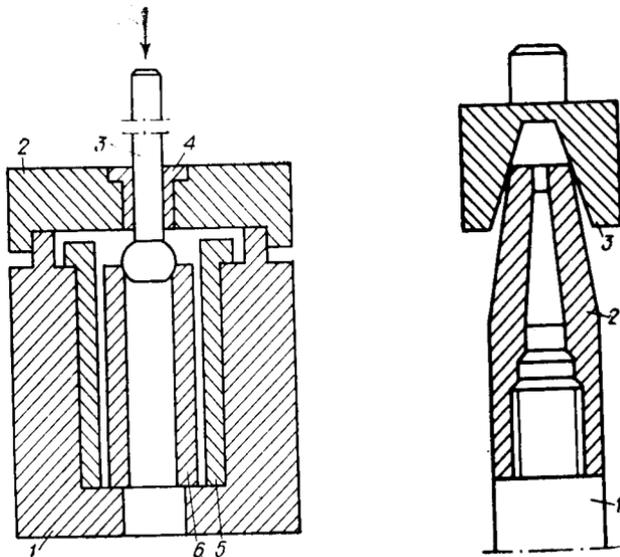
Приспособление для раздачи поршневых пальцев:
